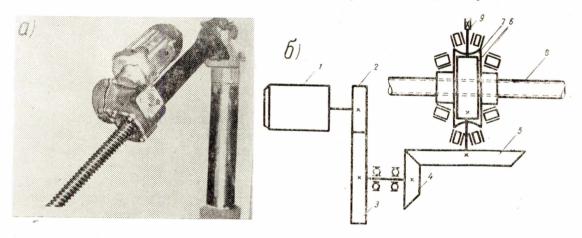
Подъемный механизм манипулятора ПММ-2 a) общий вид; δ) кинематическая схема: 1—двигатель; 2—3—4—5—зубчатый редуктор; 6—7—червячный редуктор; 8—подъемный винт; 9—вал для крепления рукоятки.
